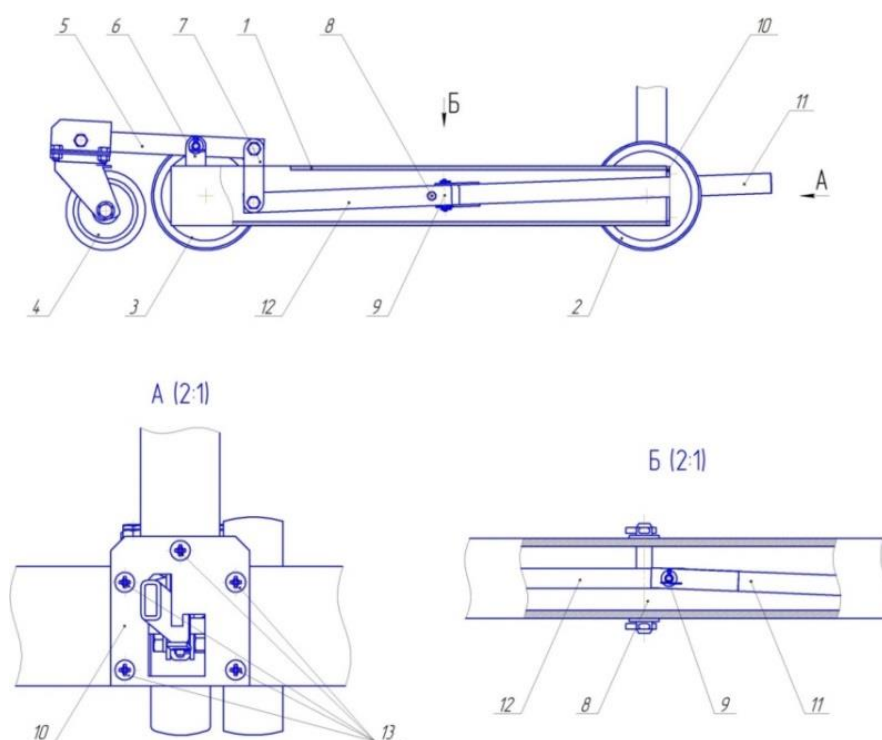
Общий вид установки для контроля и регулировки света фар
